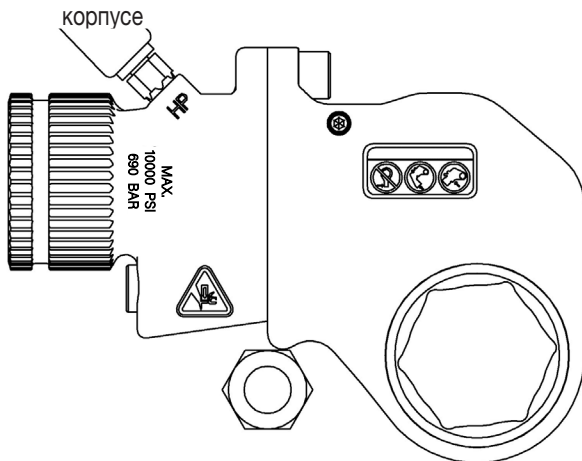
Неправильная организация упора для гайковерта с шестигранной кассетой с упорным выступом на корпусе
